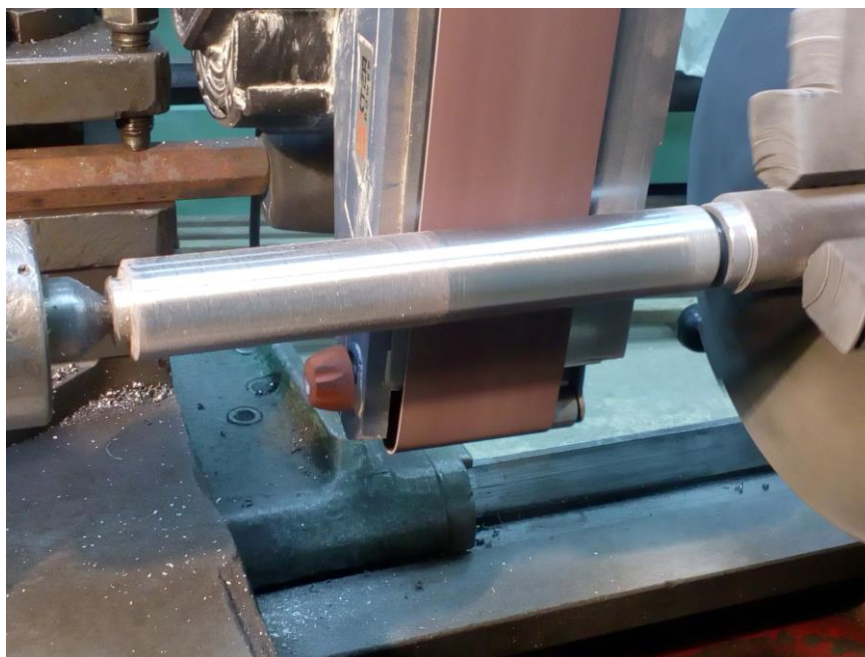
Внешний вид заготовки в процессе ленточного шлифования на токарно-винторезном станке 1К62.
